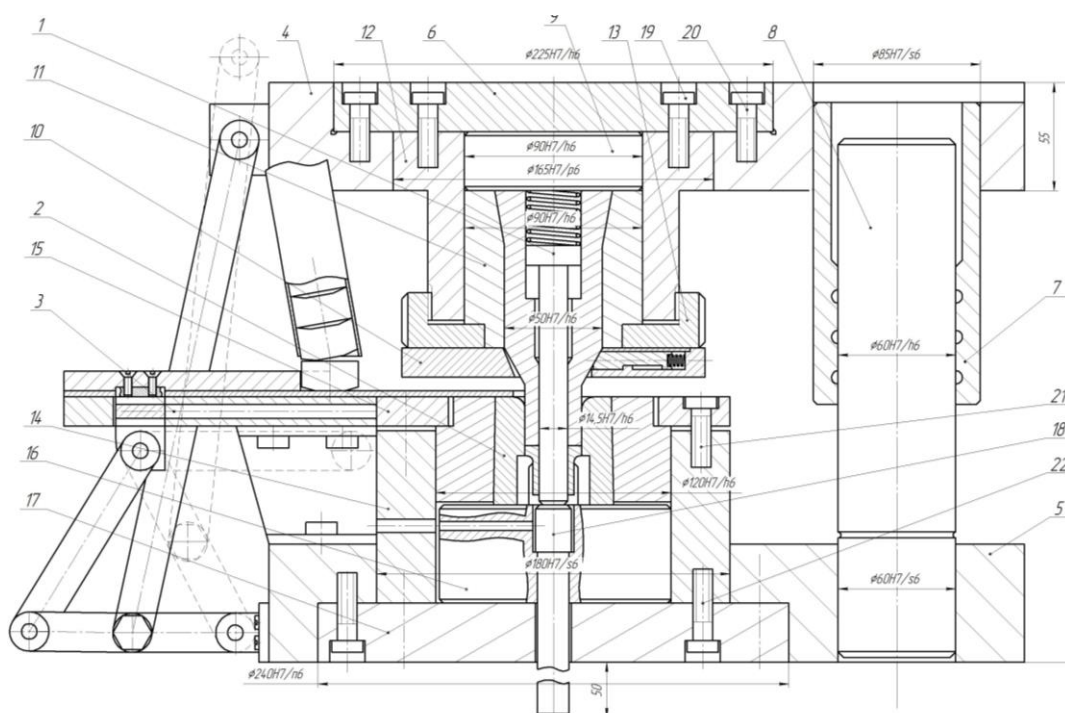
Штамп с шибрною подачею для видавлювання порожнистих деталей типу втулок
